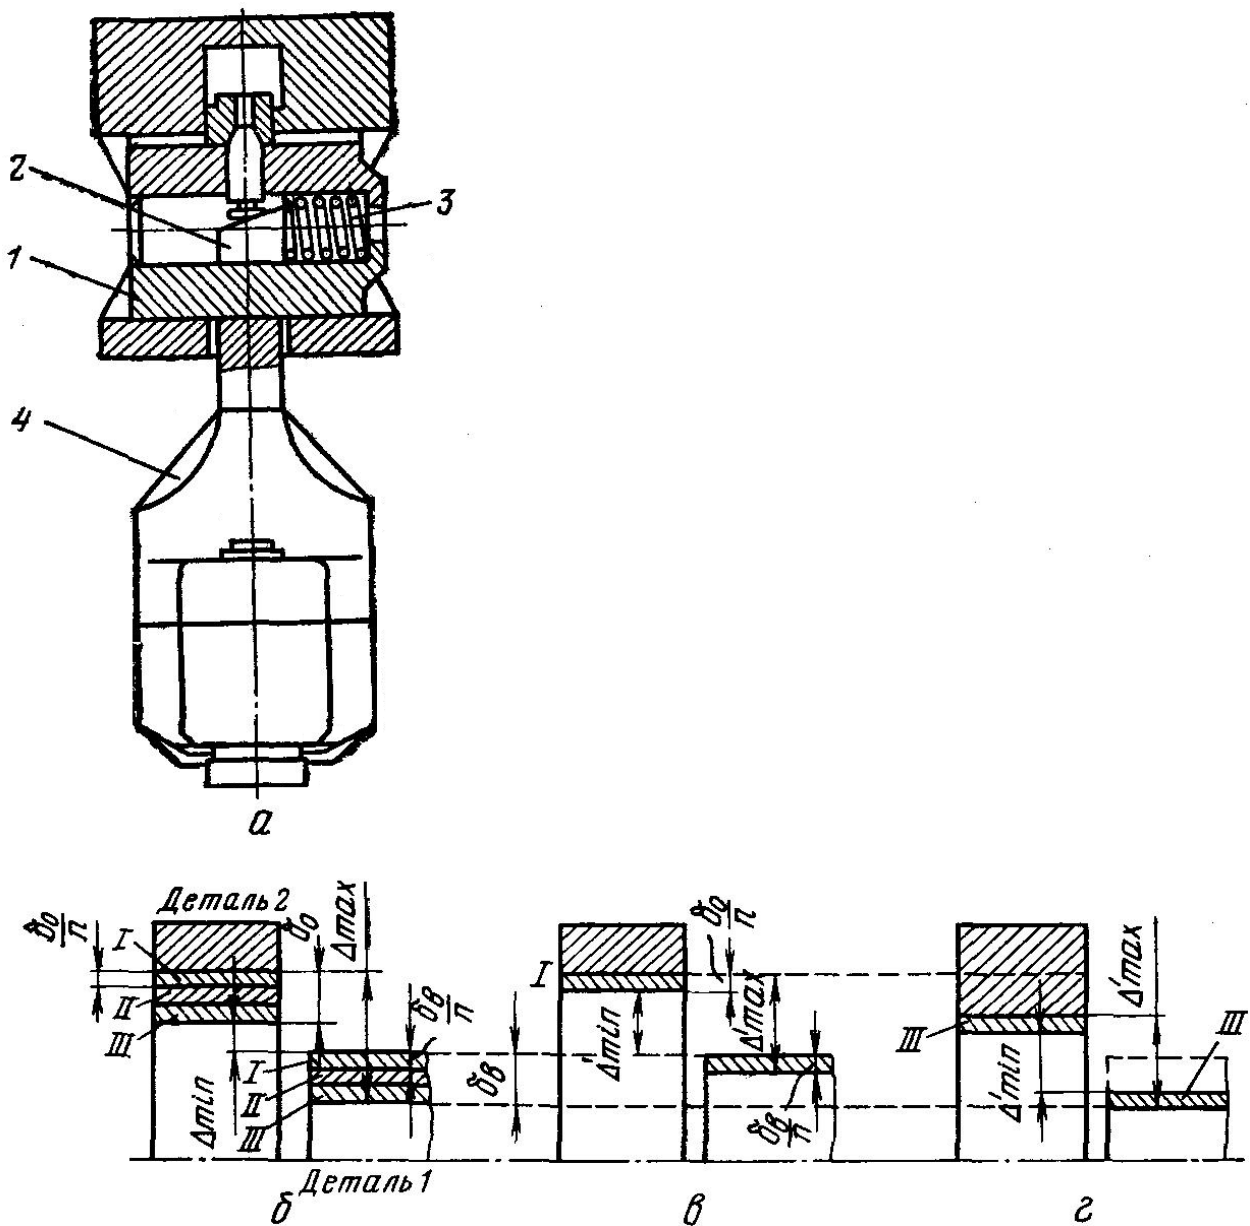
Схеми з'єднання деталей, розсортованих на розмірні групи
